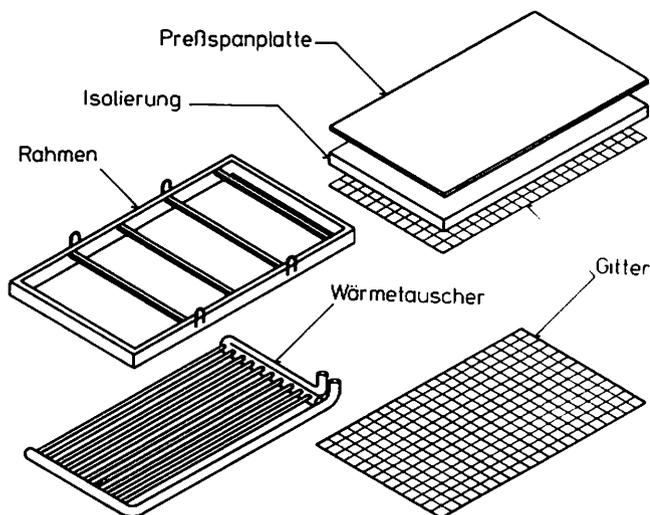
Aufbau des Wärmetauschers im Betrieb Walkemeyer
